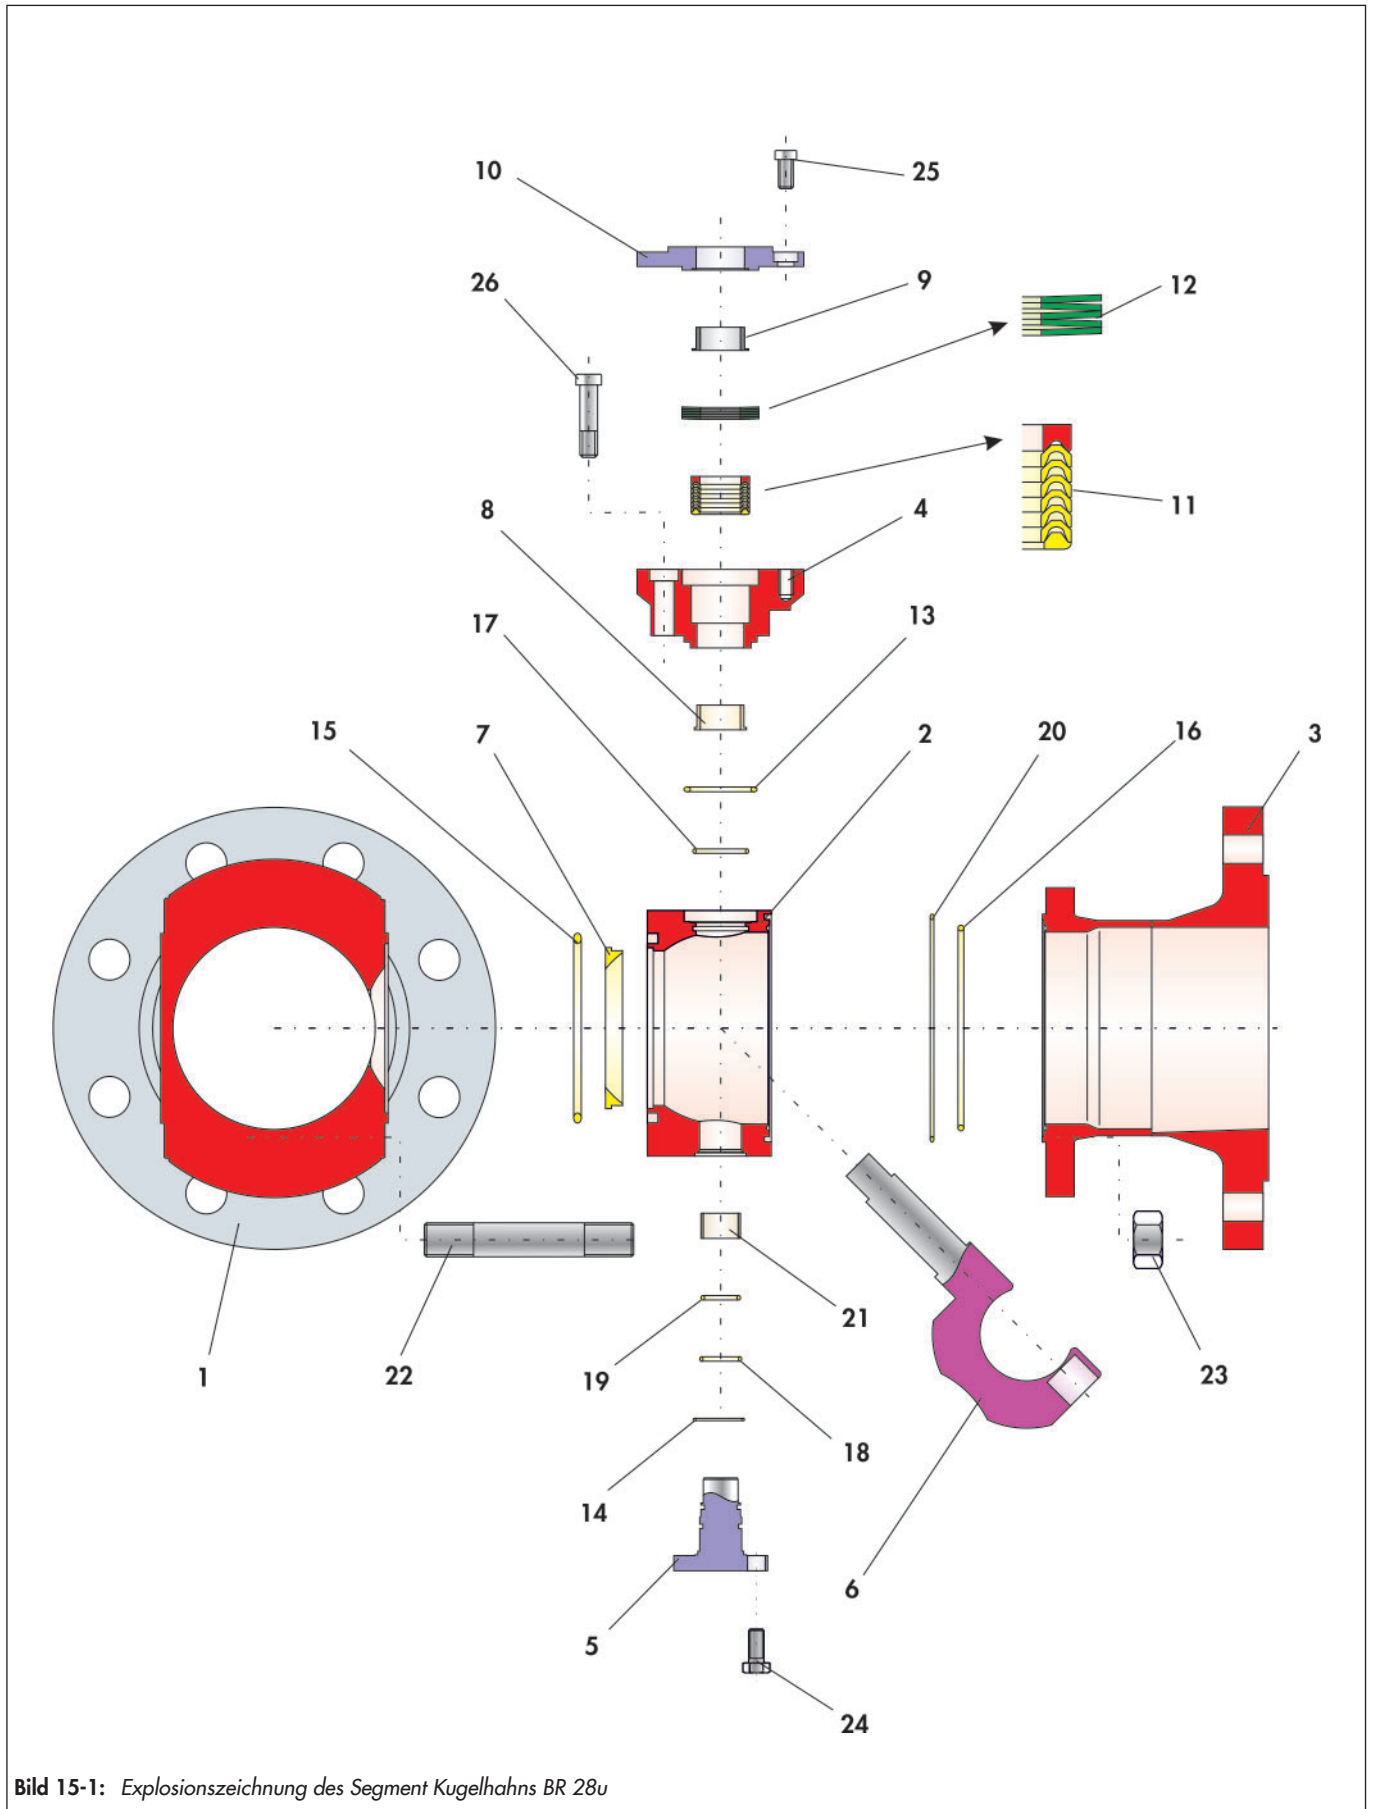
Explosionszeichnung des Segment Kugelhahns BR 28u
